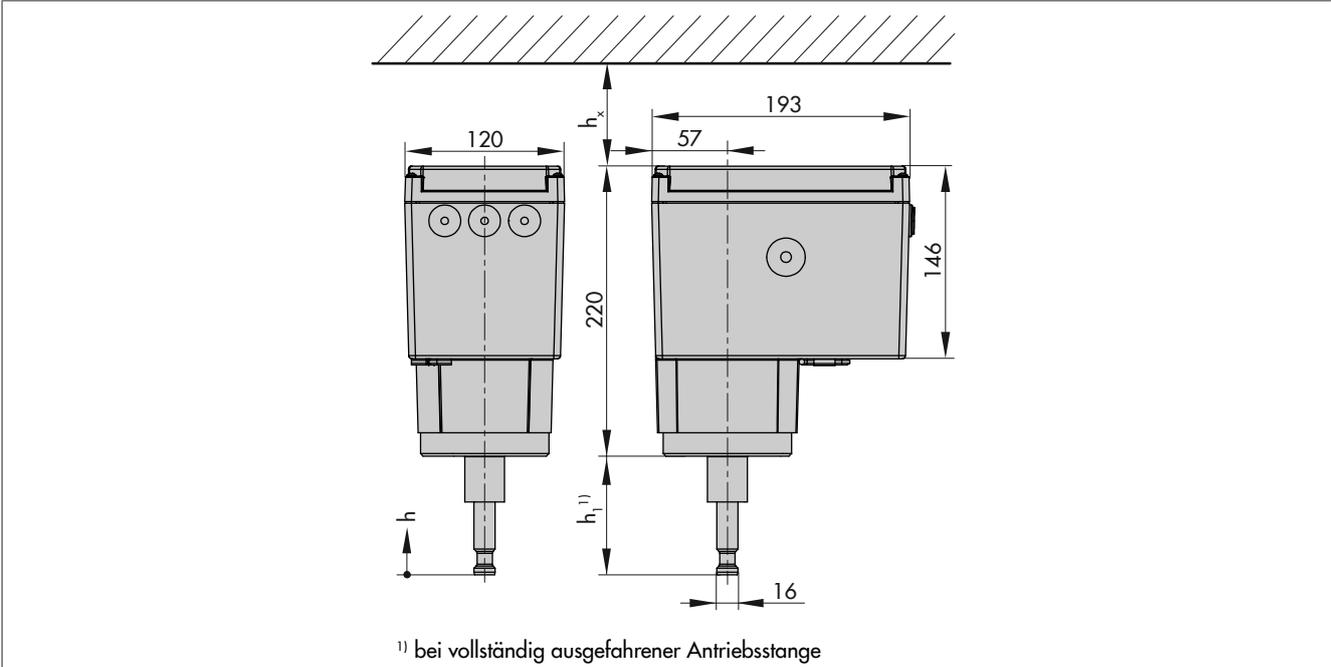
Maße in mm · Typ 3374-15, -17, -26 und -36, (Form A)
